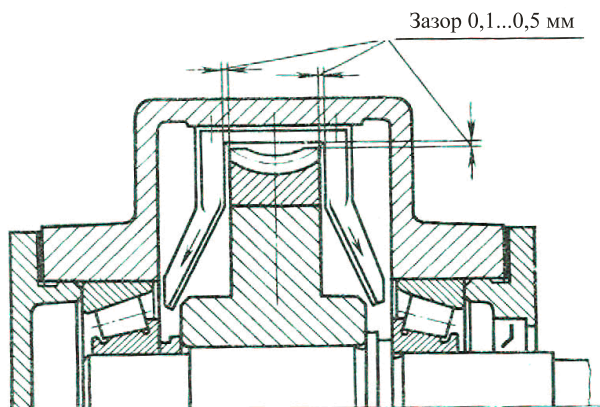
Смазывание подшипников тихоходного вала при помощи скребков с лотками
